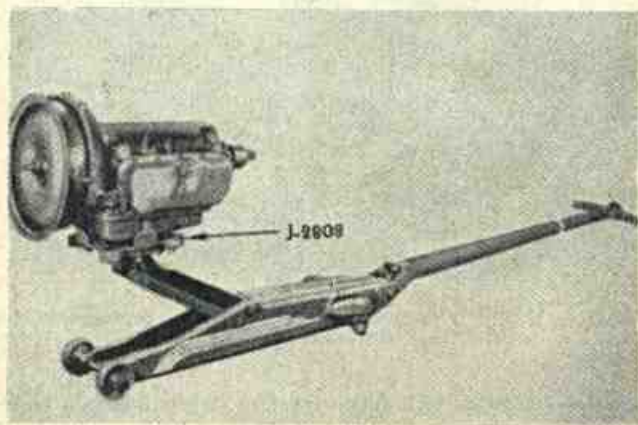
Macaco e ferramenta J-2808 para uso na retirada da transmissão.
